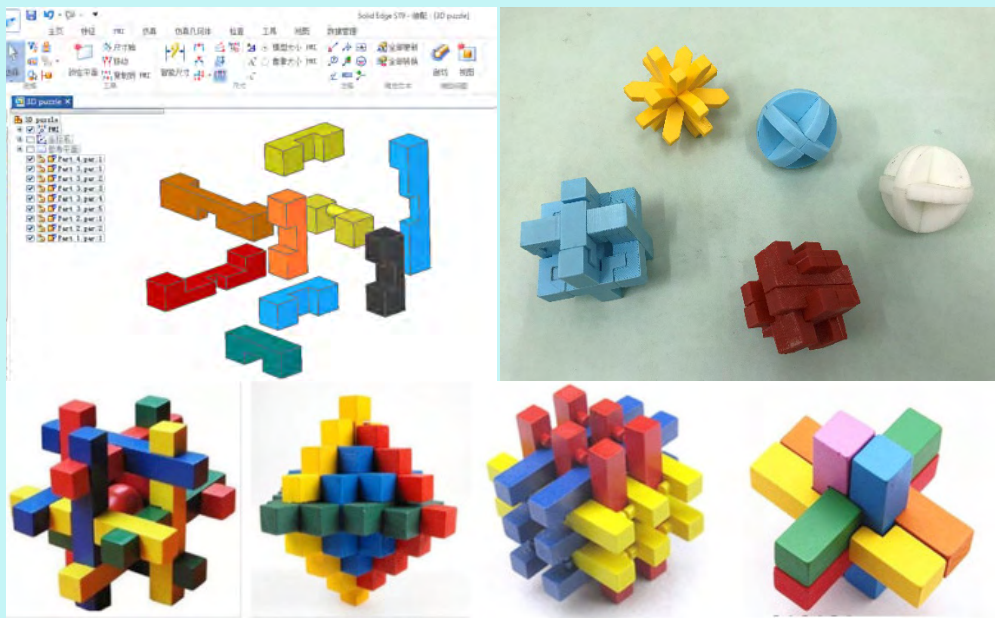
使用三维 CAD 软件进行孔明锁的建模与 3D 打印
